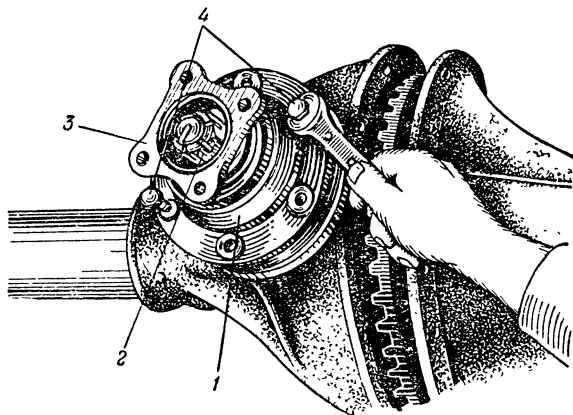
Выпрессовка муфты подшипников в сборе с ведущей шестерней при помощи двух болтов-съемников:
